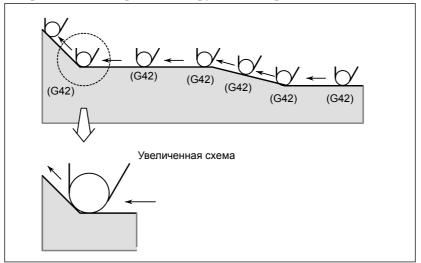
(c) Перемещение инструмента, если положение заготовки не изменяется
